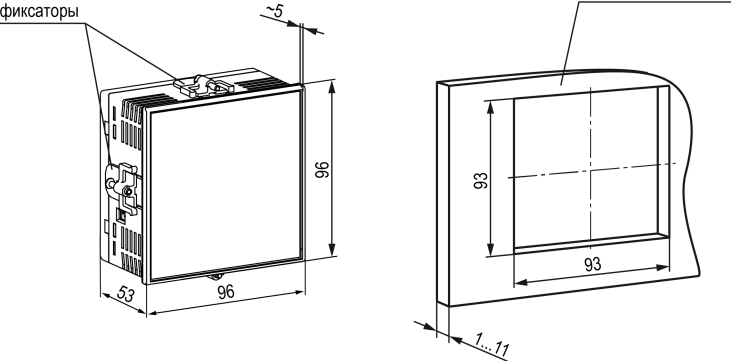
Габаритные размеры корпуса Щ1 и монтажного отверстия в щите
